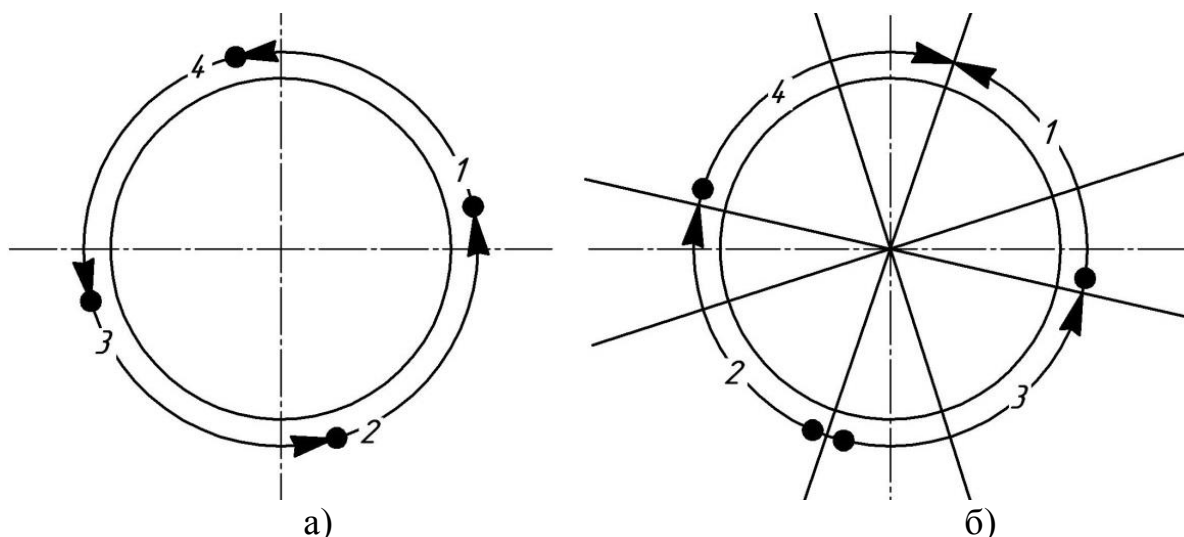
Порядок сварки участков корневого слоя шва при сварке горизонтального (а) и вертикального (б) стыка труб
